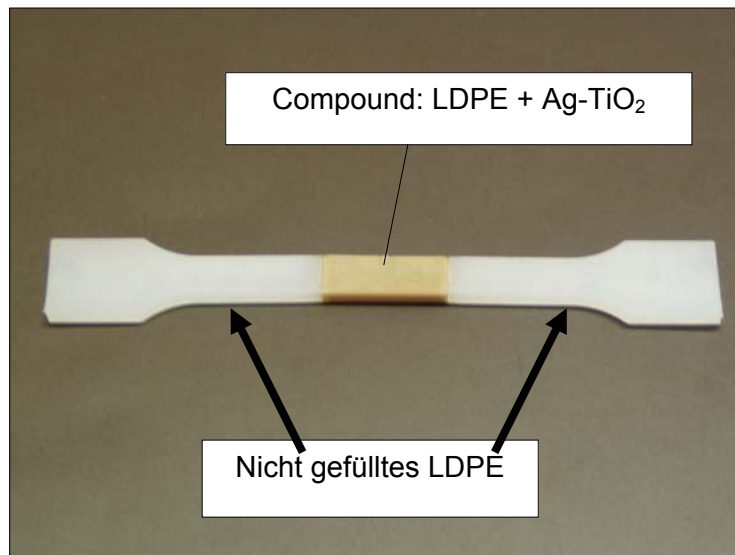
2-K Zugprüfstab für die Untersuchung der Ag-Ionenwanderung
